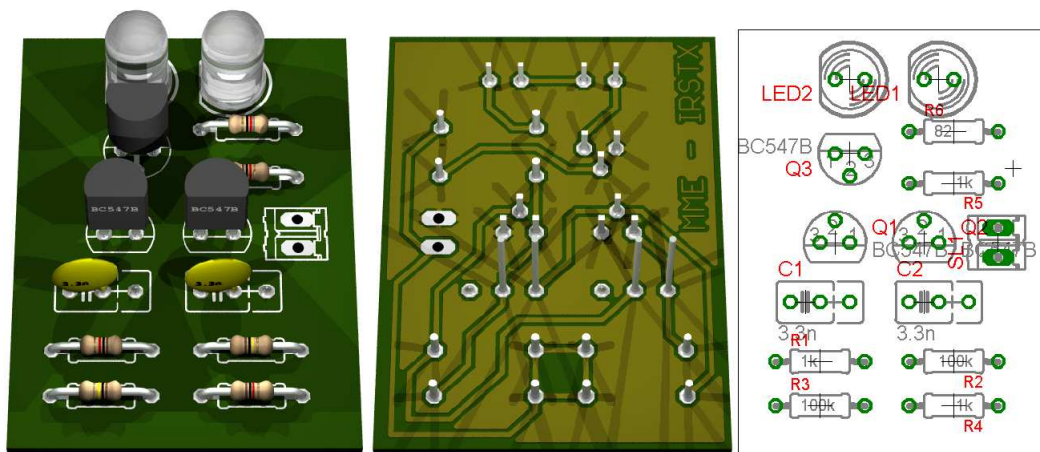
PCB trasmettitore lato componenti (sinistra) e lato rame (destra)
